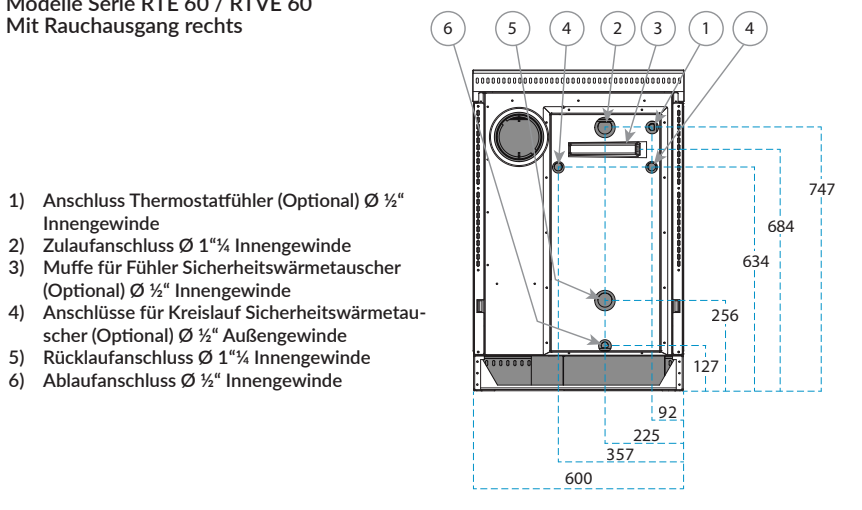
Anschlusschema der Modelle RTE 60 und RTVE 60 mit Rauchausgang rechts (Rückansicht). Bei Modellen mit Rauchausgang links befinden sich die Anschlüsse symmetrisch.
